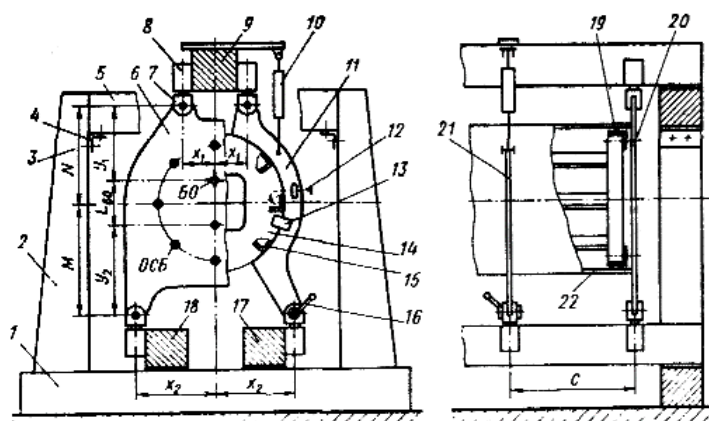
Эскиз сборно-разборного приспособления (СРП)
